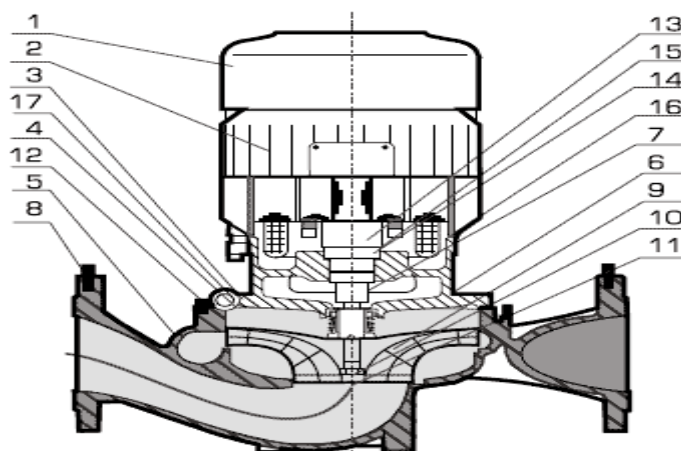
Общий вид насоса ЦМЛ: 1 – крышка вентилятора; 2 – электродвигатель; 3 – проставка; 4 – прокладка; 5 – корпус спиральный; 6 – кран Маевского; 7 – торцевое уплотнение; 8 – вывод на датчик давления с резьбовой пробкой; 9 – рабочее место; 10 – шайба; 11 – гайка; 12 – болт; 13 – вал; 14 – отбойник (манжета); 15 – крышка (кольцо стопорное); 16 – масленка; 17 – рым-болт
